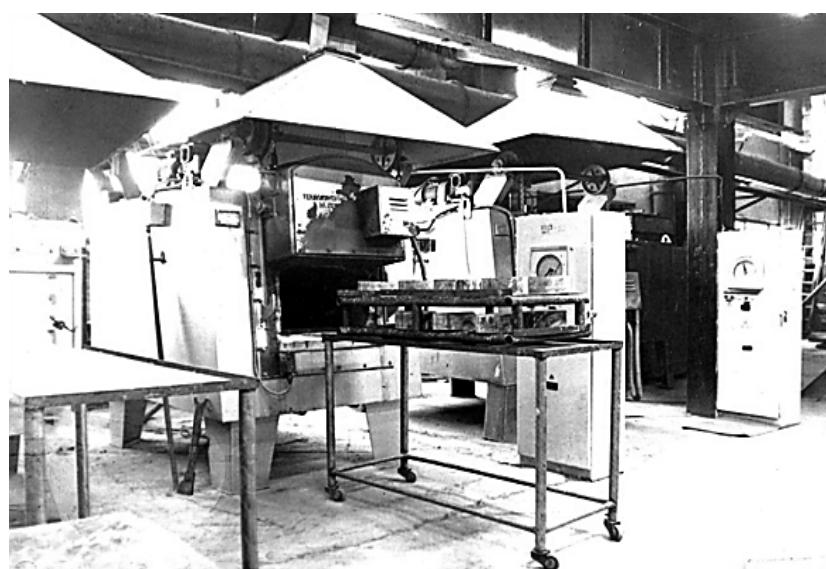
Печи для обжига полноразмерных металлических катализаторов
